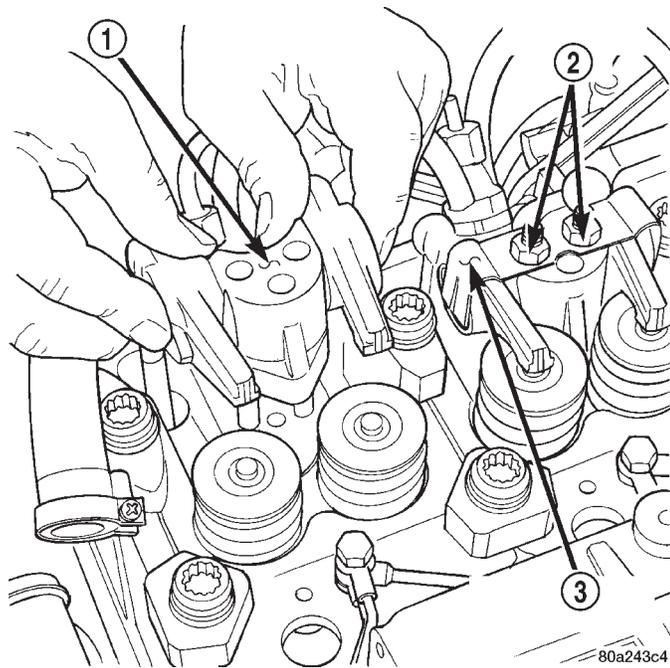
Montagewerkzeug VM.1012B für Einspritzdüse
